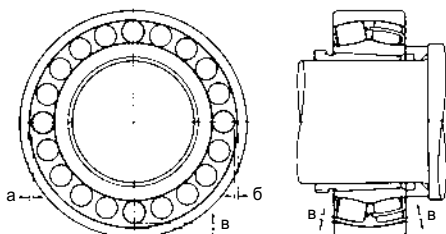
Измерение зазора в большом сферическом подшипнике с бочкообразными роликами
